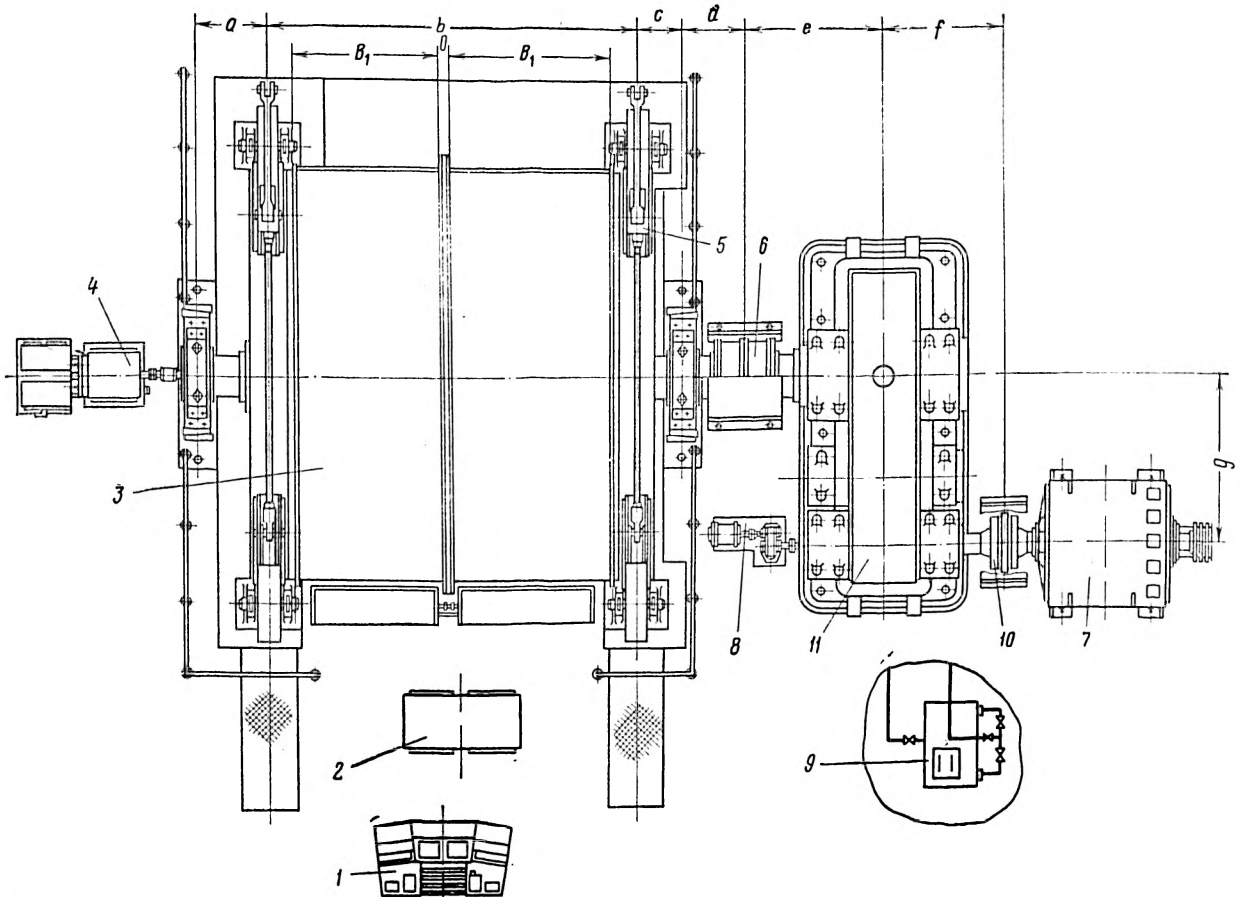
Общий вид двухбарабанных подъемных машин 2Ц-4×1,8; 2Ц-4×2,3 с двухступенчатым редуктором ЦД-20 (вид в плане):
